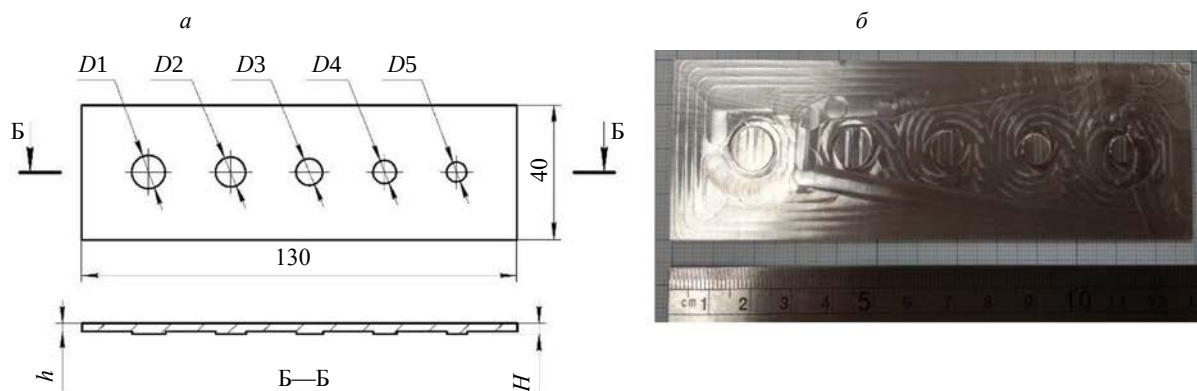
Образец настроечный с имитаторами сварных зон различного диаметра: эскиз (а); общий вид (б).
